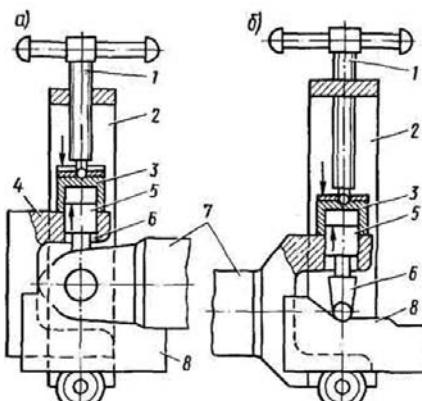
Выпрессовка подшипников из фланца-вилки (а) и из вилки вала (б): 1 — винт; 2 — раздвижные стойки; 3 — стакан; 4 — фланец-вилка карданного вала; 5 — подшипник; 6 — крестовина; 7 — вилка карданного вала; 8 — опорная призма
